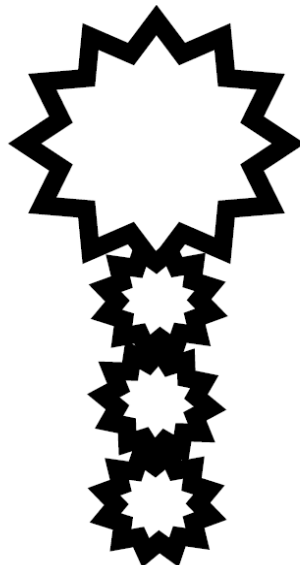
Принципиальная схема расположения шестерней в редукторе
